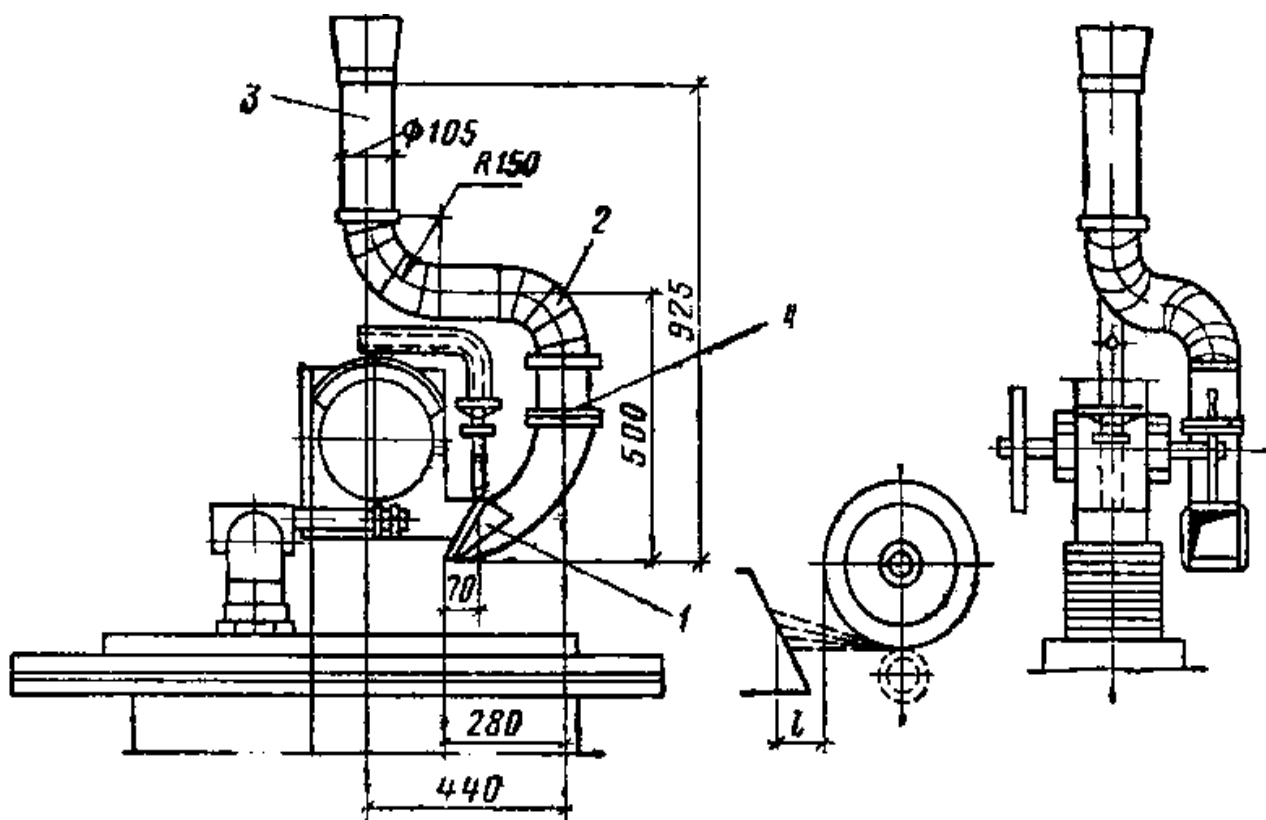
Местный отсос от универсально-заточного станка 3А-64
